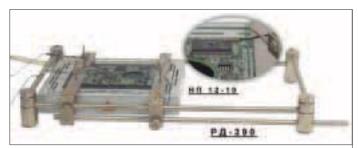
Прибор нижнего подогрева ПП НП 12-10 и рамочный держатель плат РД-390
